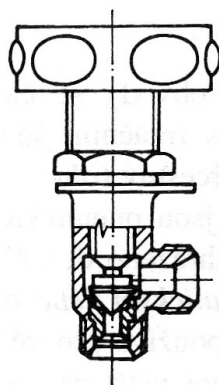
Jednosměrný ventil s destičkou [2]
